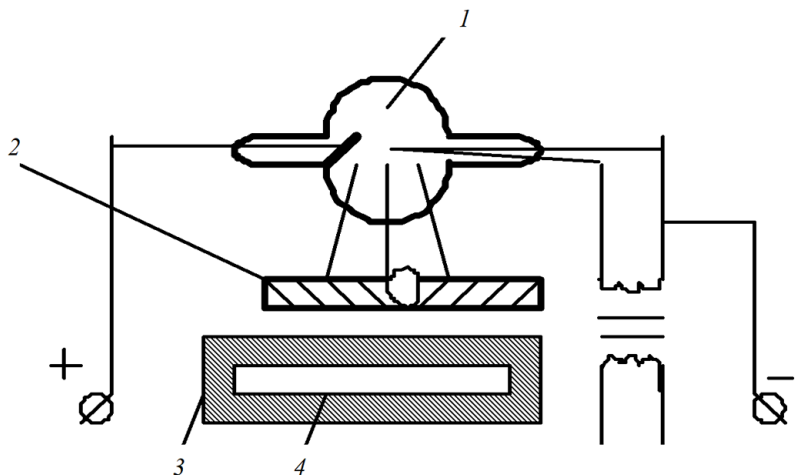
Рентгенографический контроль сварных соединений:
